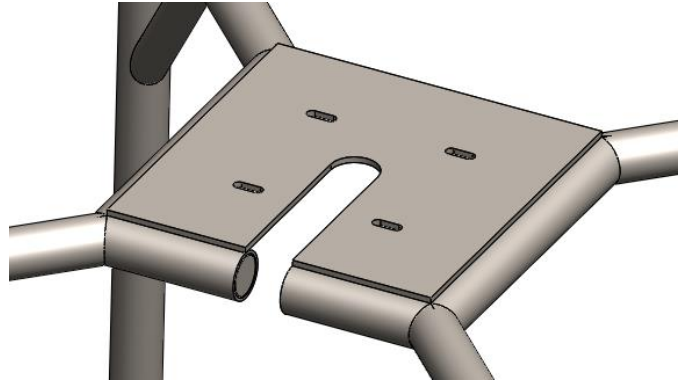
Placa de 3/16" soldada a la torre para la ubicación de los fijadores.
